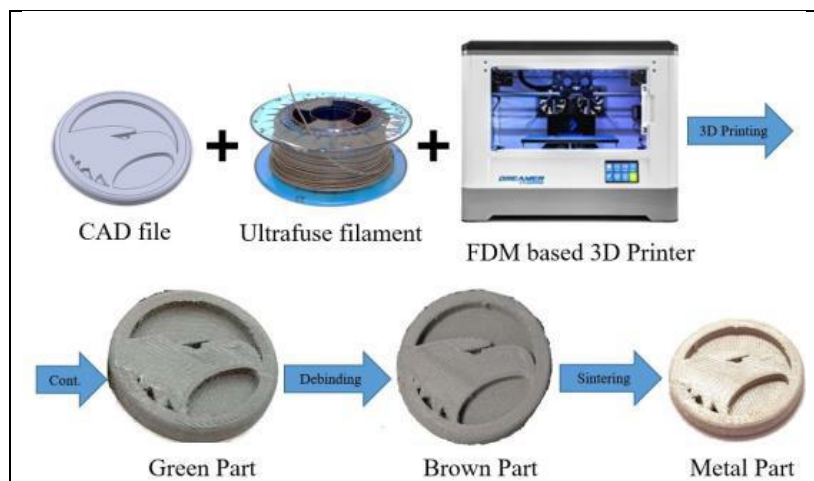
Processo di stampa 3d utilizzando un filamento "metallico" [66]
